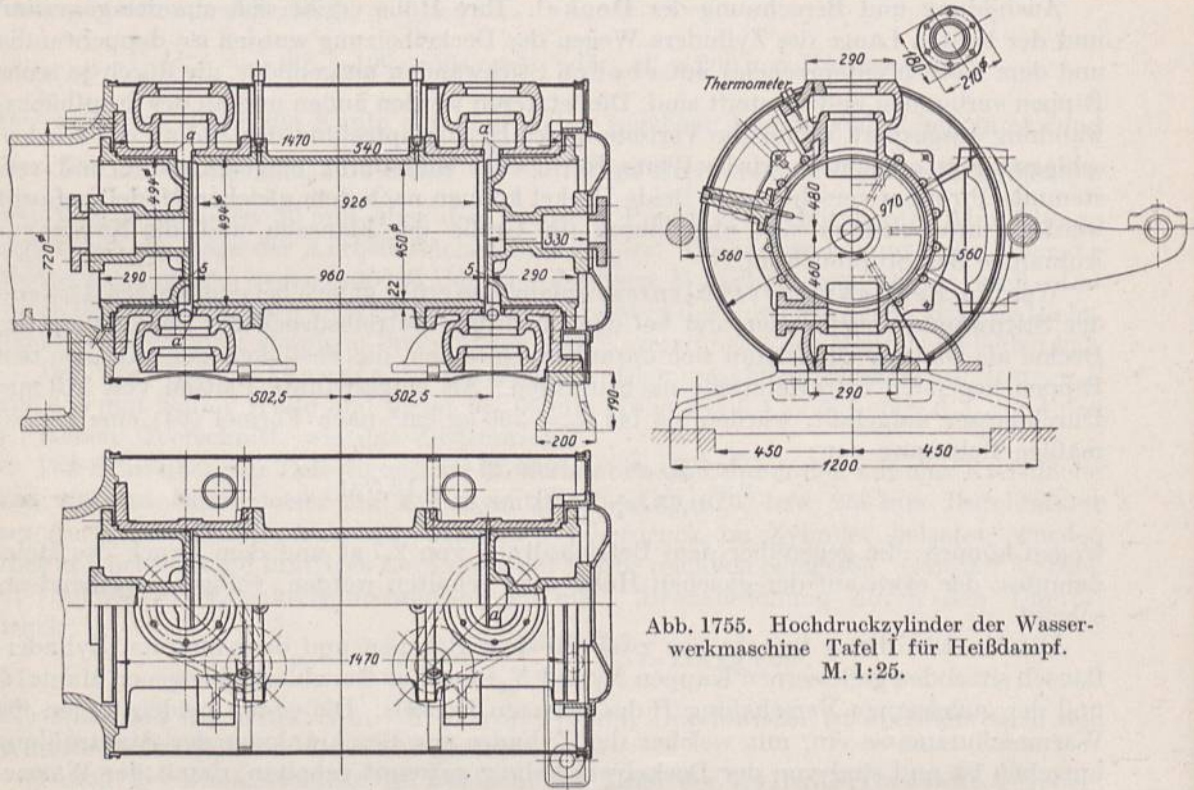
Hochdruckzylinder der Wasserwerkmaschine Tafel I für Heißdampf.
